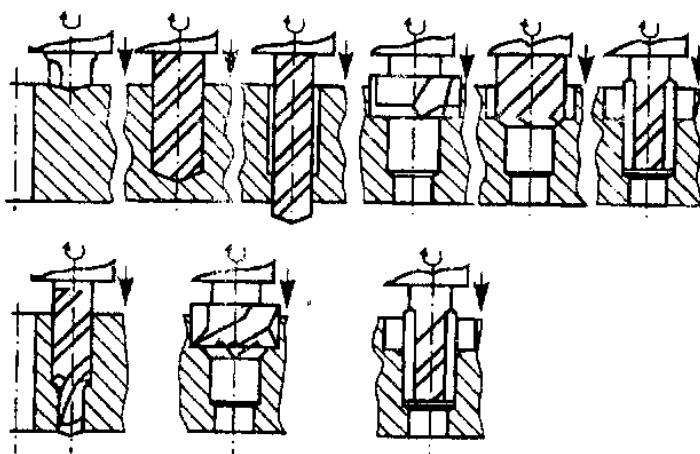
Можливі варіанти виготовлення модуля поверхонь базуючих 211
